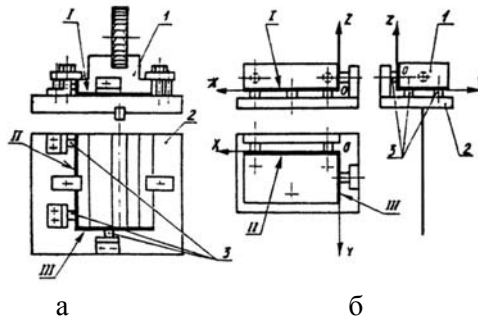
Базирование заготовок по плоским базовым поверхностям в приспособлениях: I – установочная; II – направляющая; III – опорная базы заготовки; 1 – обрабатываемая заготовка; 2 – корпус приспособления; 3 – установочные элементы – опоры приспособления
